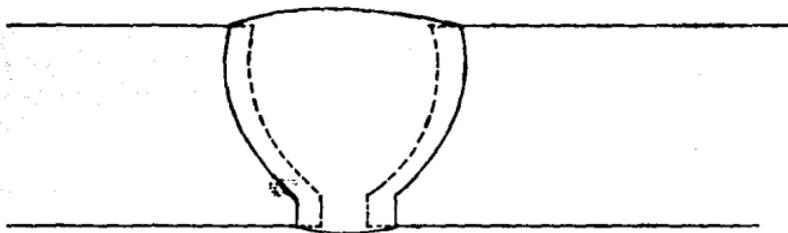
Soldadura con Bisel Sencillo en U
